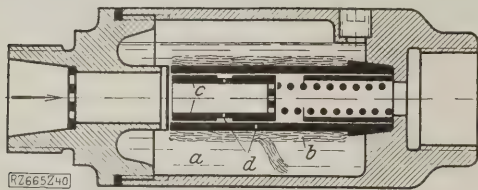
Schmiervorrichtung der Maschinenfabrik Hausherr, Hinselmann & Co.
